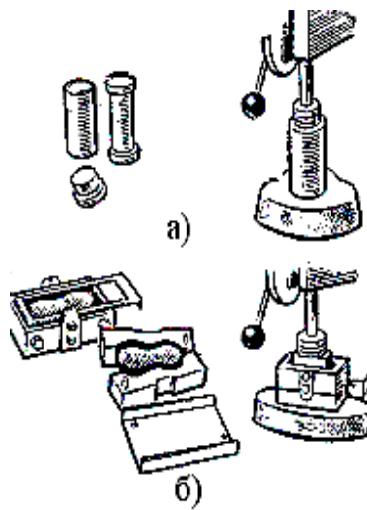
Пристрій для виготовлення на копрі контрольних зразків
